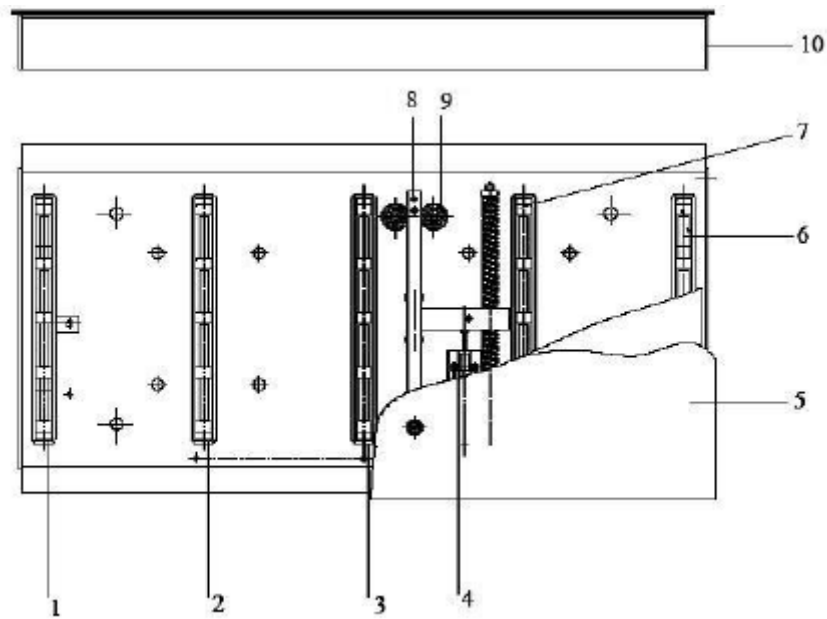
Конструкція станда для експрес-діагностики положення коліс: 1,2,3,6,7 – полозок; 4 – вимірювальний датчик; 5 – вимірювальна плита; 8 – пристрій зрушення; 9 – напрямні; 10 – короб
